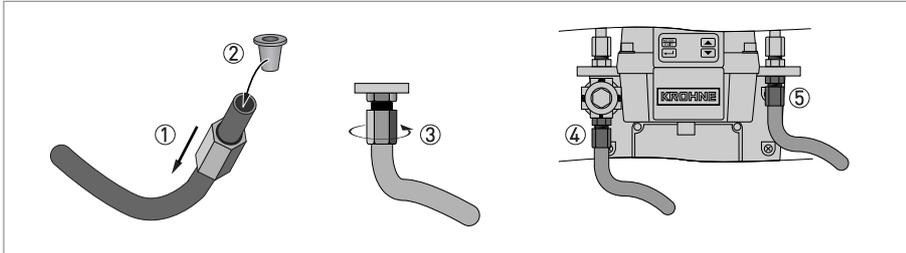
Assemblage des pièces et branchement des tuyaux
